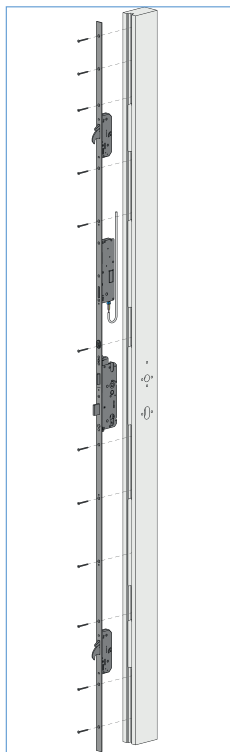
Montaje STV-EAV4/EAV4+
